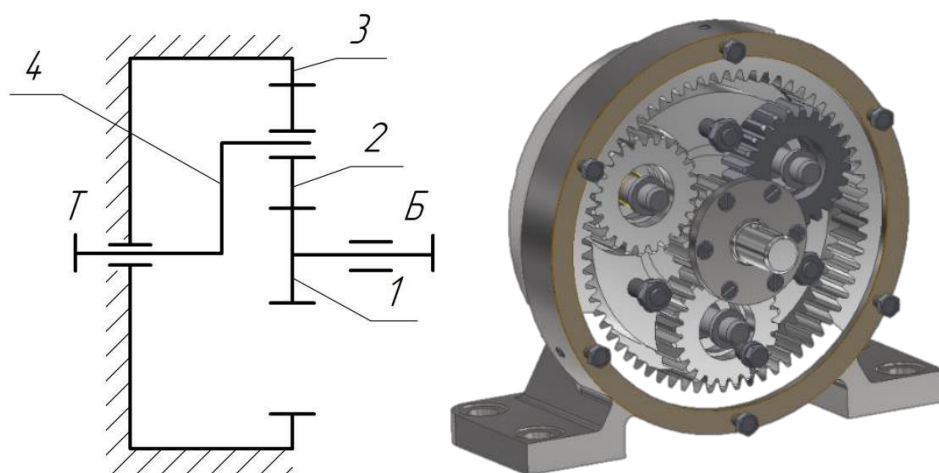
Одноступенчатый планетарный редуктор
